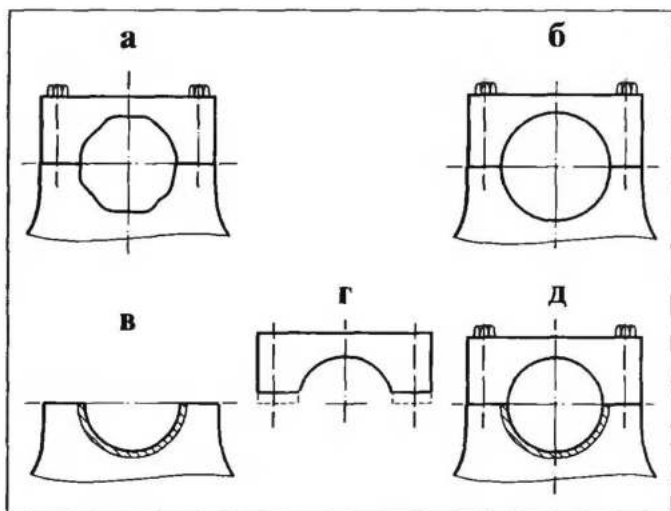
Возможный способ ремонта опоры распределительного вала с помощью алюминиевого вкладыша: а — поврежденная опора; б — растачивание отверстия в больший размер с использованием технологической крышки; в — установка и подгонка вкладыша; г — подрезка плоскости стыка крышки; д — окончательная обработка отверстия в требуемый размер
